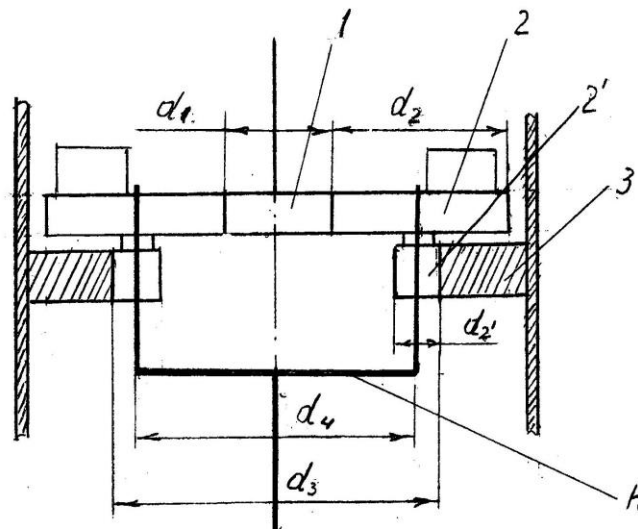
Розрахункова схема планетарного вібробудника крутильних коливань.
